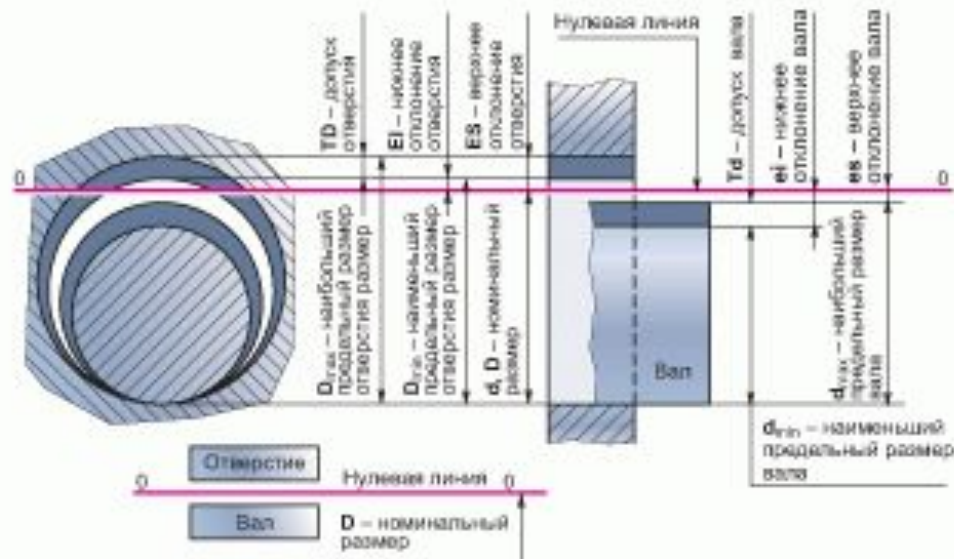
Схема расположения полей допусков, сопрягаемых деталей (соединение с зазором)
